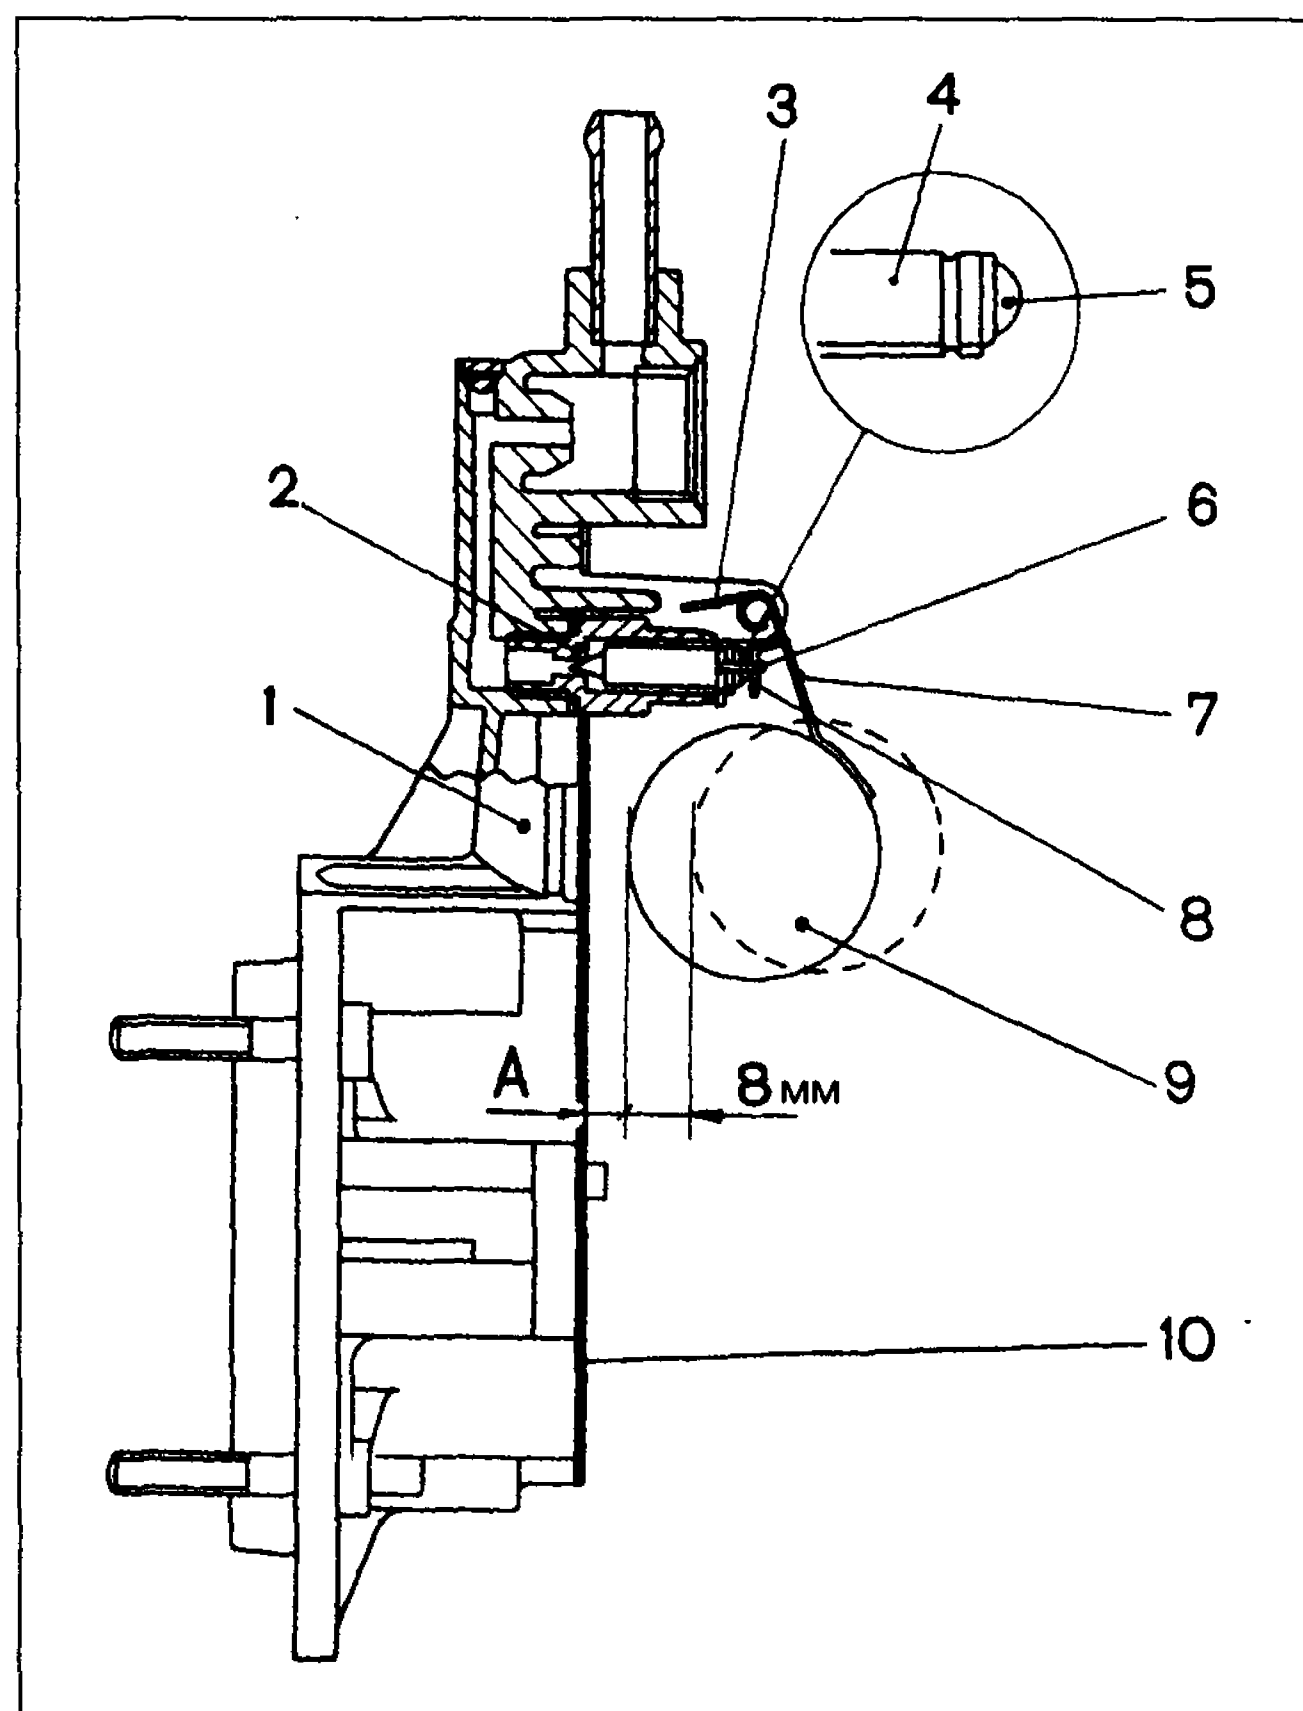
Установка уровня топлива в поплавковой камере карбюратора:
